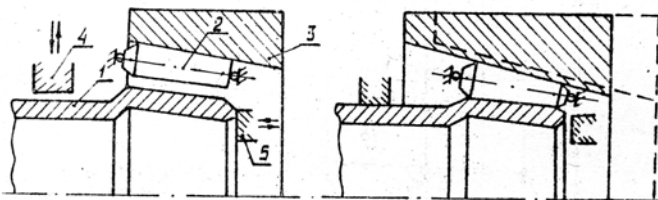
Схема наружной калибровки концов труб: 1 – труба;
